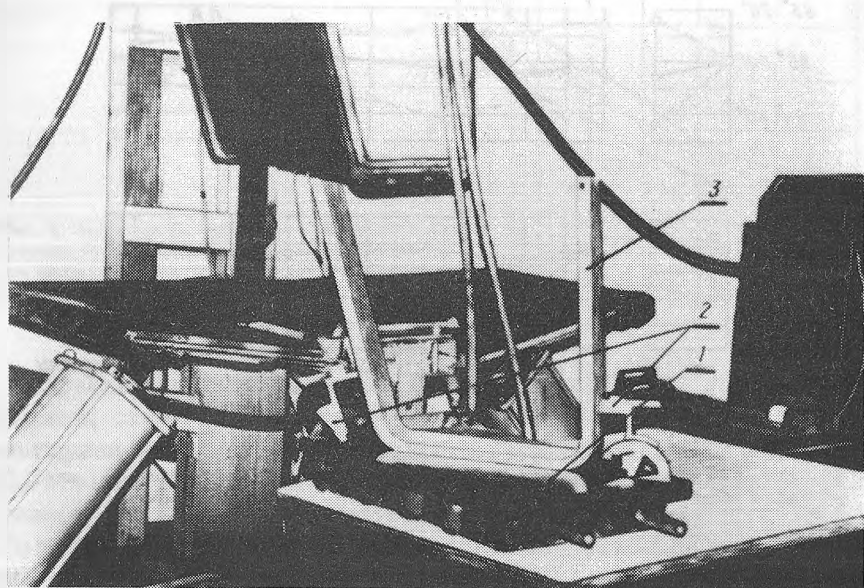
Измерение углов гнуктоклееных заготовок: 1 – поверочная плита; 2 – угломеры; 3 – гнуктоклееная заготовка.
